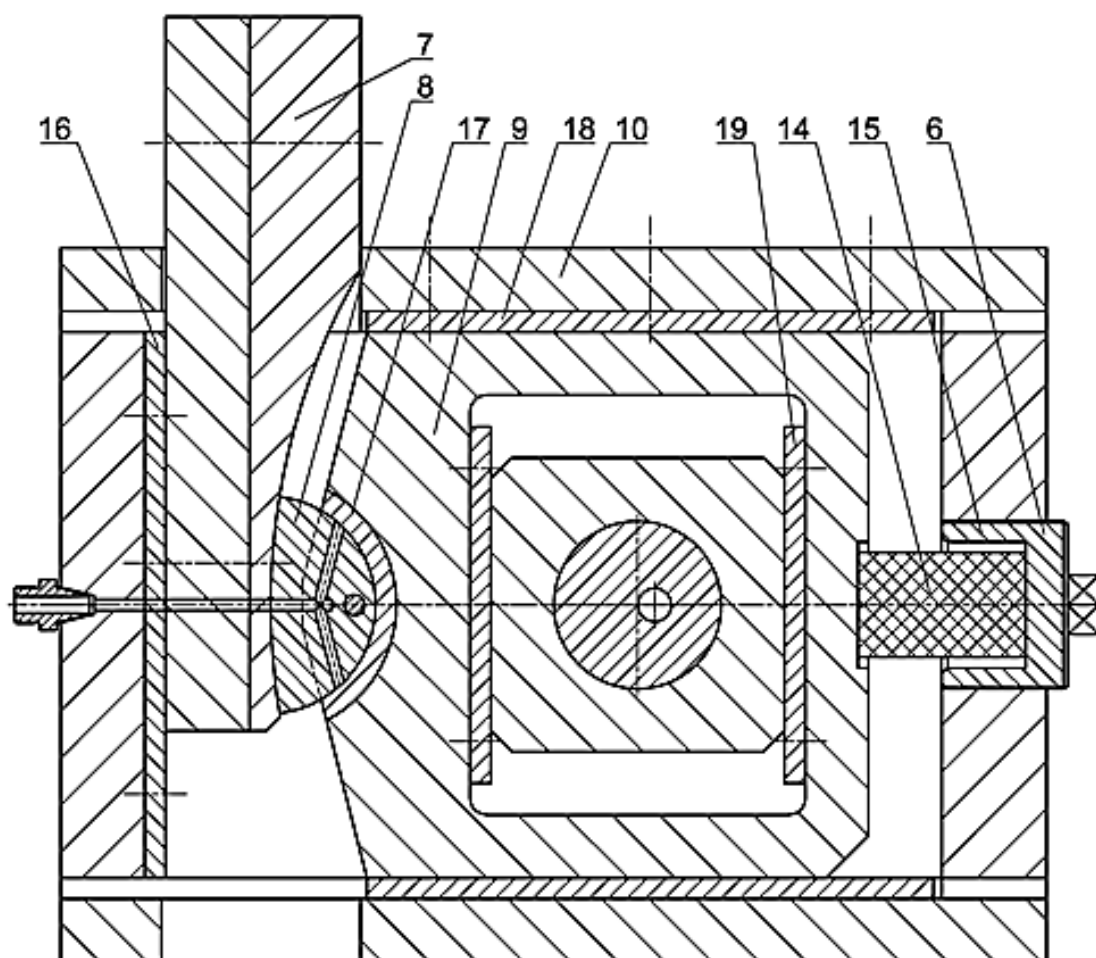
Пристрій з клиношарнірним механізмом у сполученні з рамним повзуном (конструктивний вузол П4) [10, 11]
